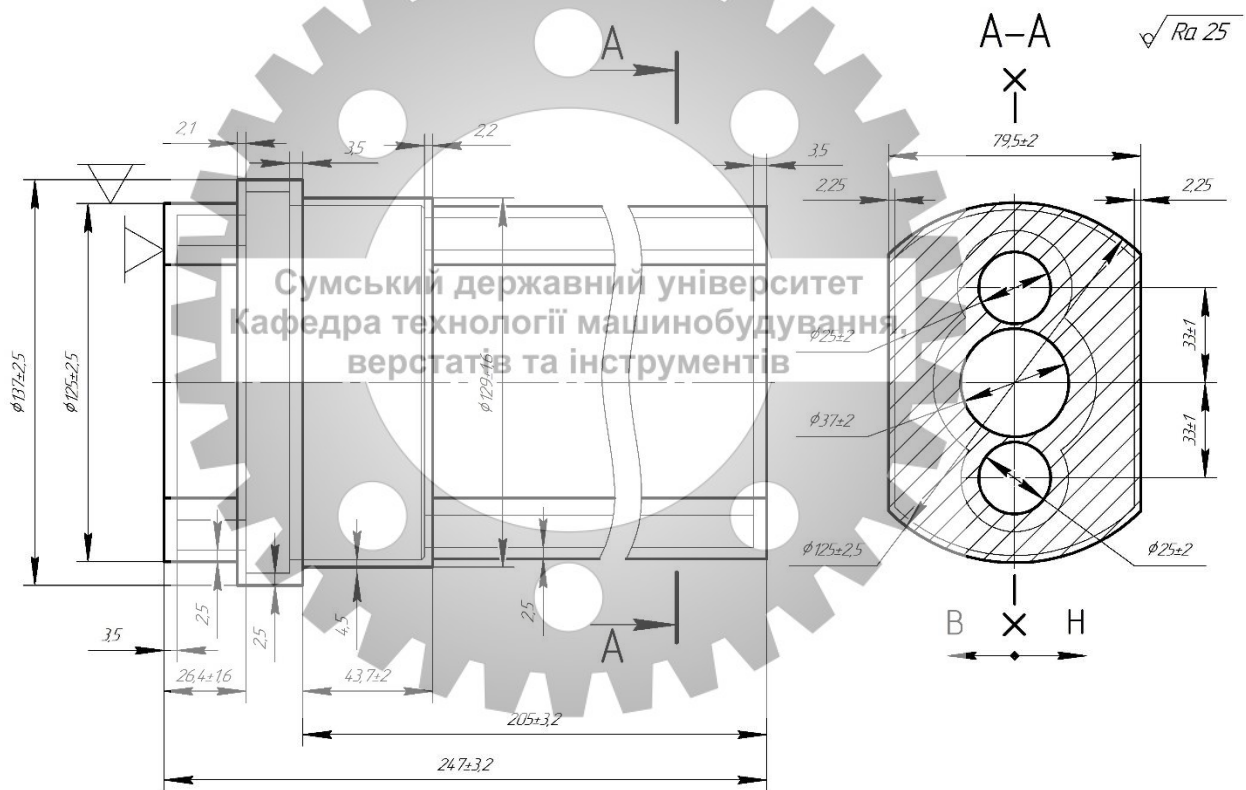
Ескіз заготовки запропонованого способу виготовлення
